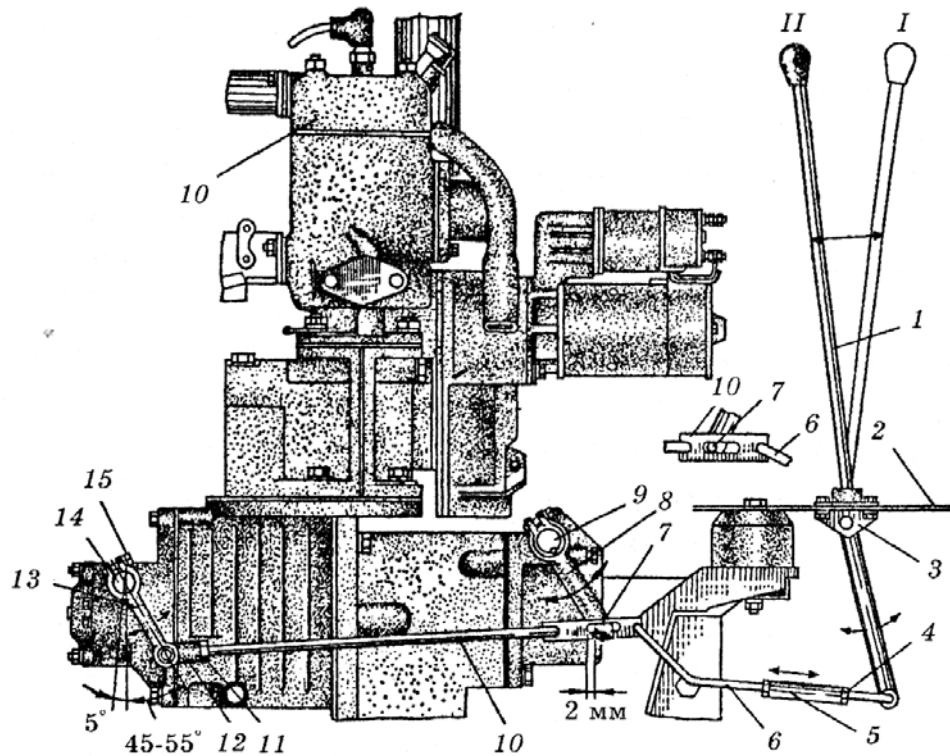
Механізм дистанційного керування редуктором пускового двигуна трактора МТЗ-80:
